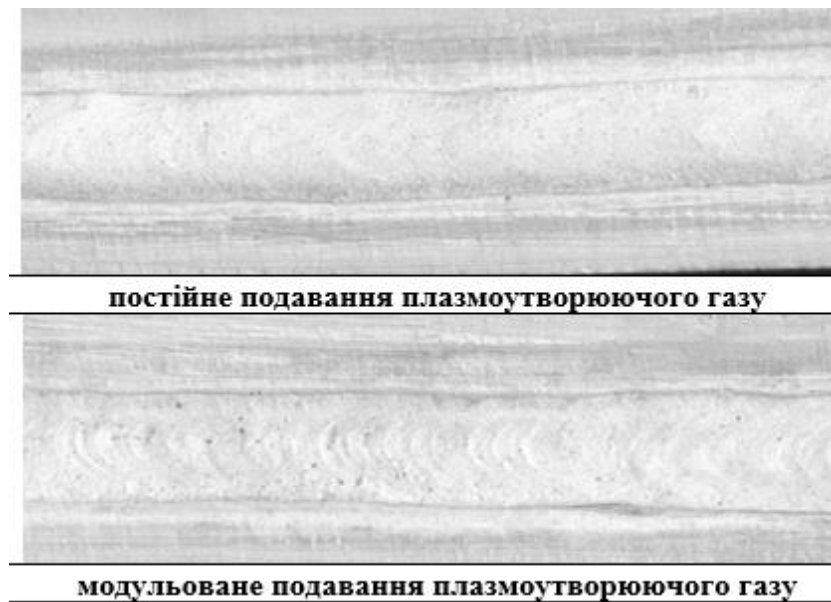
Зовнішній вигляд верхньої частини зварного з'єднання із листів алюміній-літійового сплаву 1460 (Al-Cu-Li) товщиною 3 мм, отриманого плазмодуговим зварюванням різнополярним асиметричним струмом при швидкості зварювання 200 см/хв (120 м/ч).
